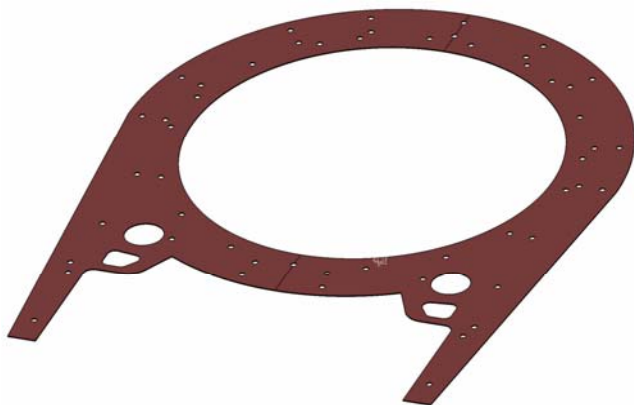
3D model konstrukcije obrtne platforme, /2/
